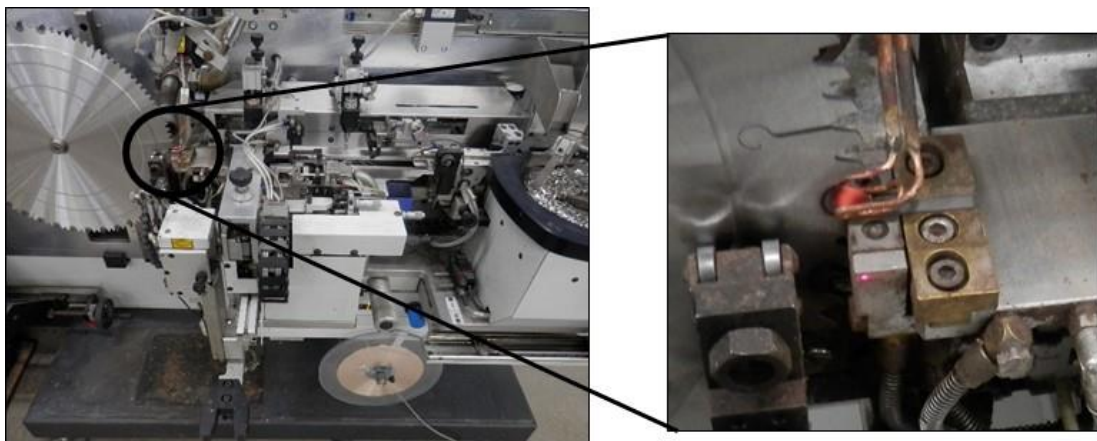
Operação de soldadura das pastilhas de corte ao corpo da serra.
